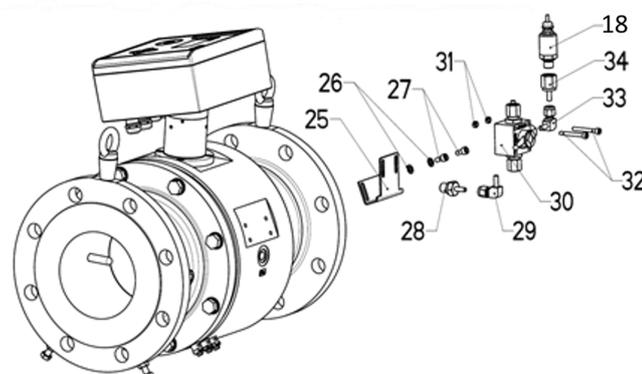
Ausführung 3-Wegehahn mit Druckaufnehmer
